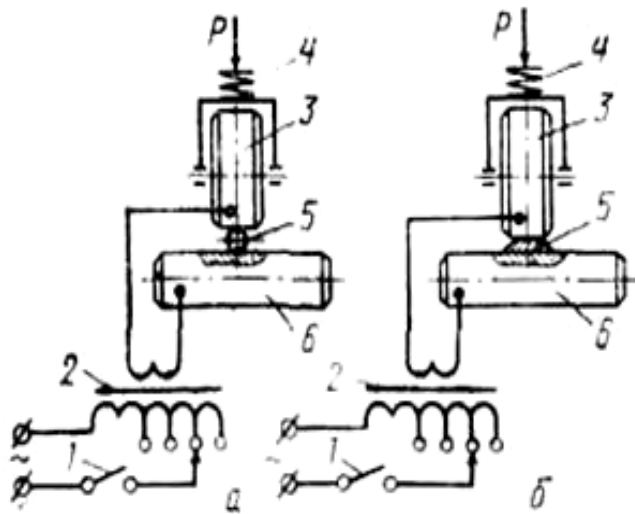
Схема установки електроконтактного наплавлення: *а* — початковий стан; *б* — кінцевий стан; 1 — переривник струму; 2 — трансформатор; 3 — наплавляючий ролик; 4 — амортизатор; 5 — присадковий дріт; 6 — зразок
